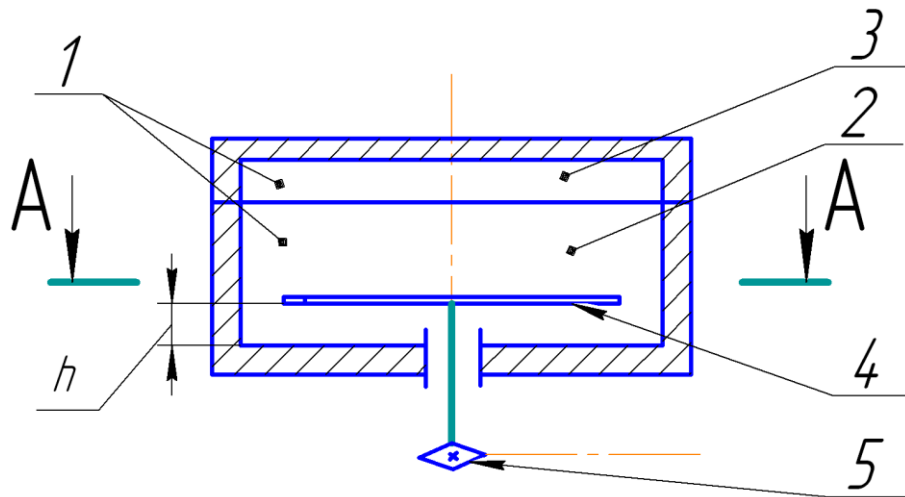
Схема пристрою для обмолоту з робочим органом у вигляді плоскої пластини, вигляд спереду: 1 – молотильна камера; 2 – корпус; 3 – кришка; 4 – робочий орган у вигляді ротора-пластини; 5 – привід в обертання ротора-пластини.
